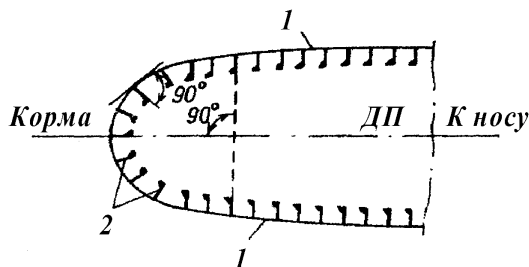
Установка шпангоутов: 1 – бортная обшивка, 2 – поворотные шпангоуты
